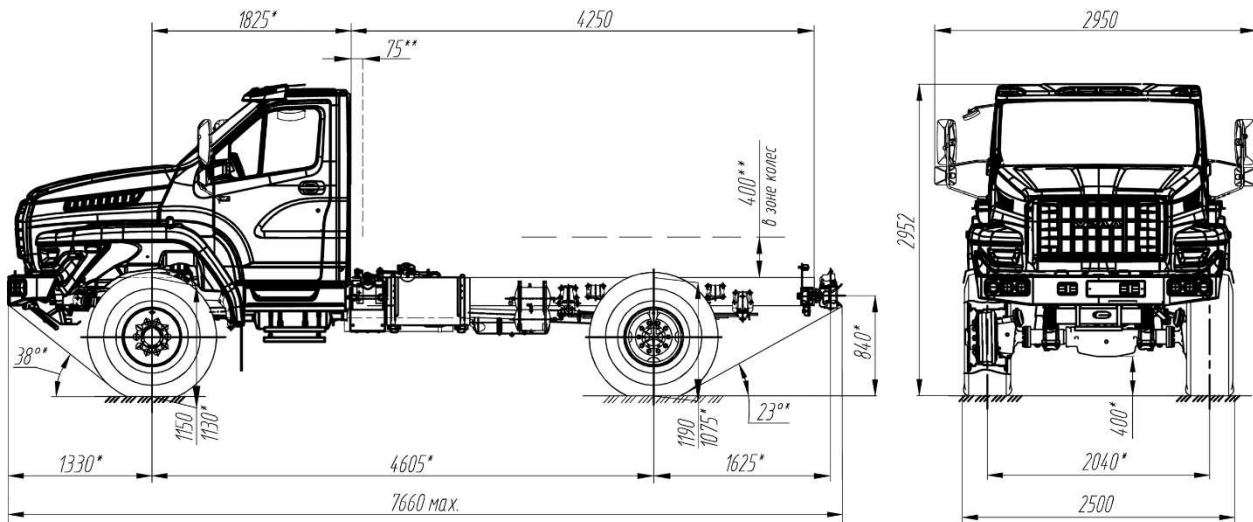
Габаритные размеры шасси Урал-43206-6151-71/73
